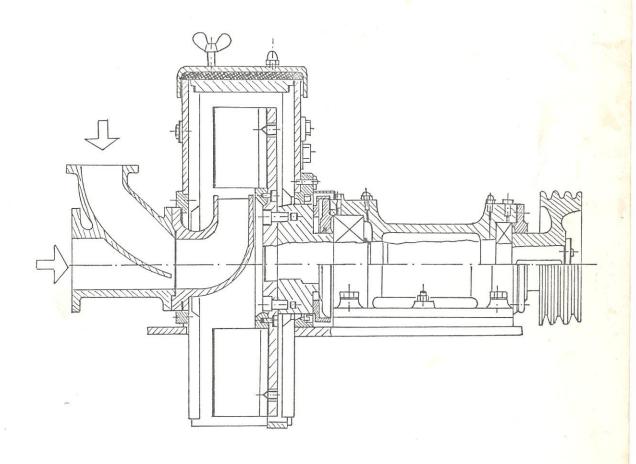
TURBINA TIPO DESLIZADORA DE UNICO DISCO
